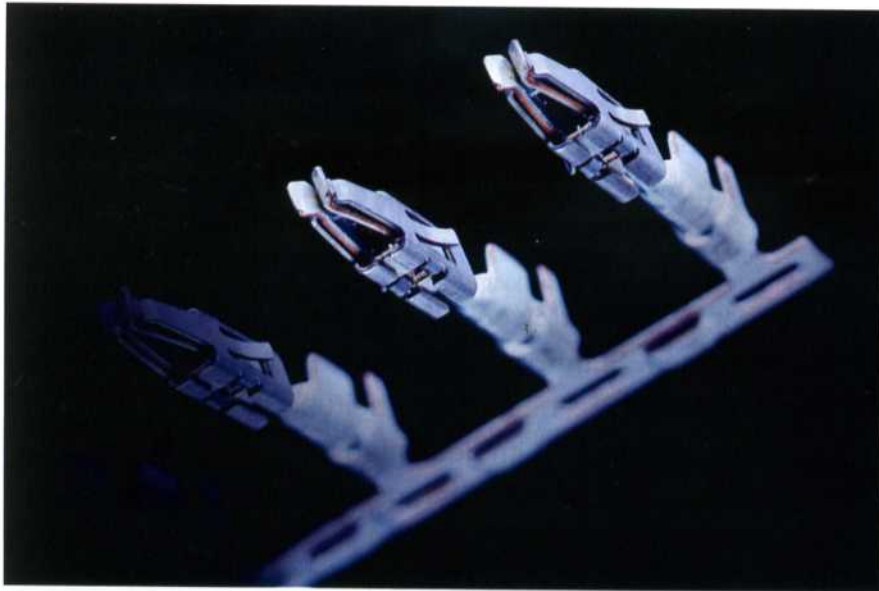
Ultralangstreckenläufer: Mit den Werkzeugen von Schroeder+Bauer werden oft bis zu 2 Mrd. Teile gefertigt (Werkbilder: TECNO.team GmbH, Kirchentellinsfurt)
